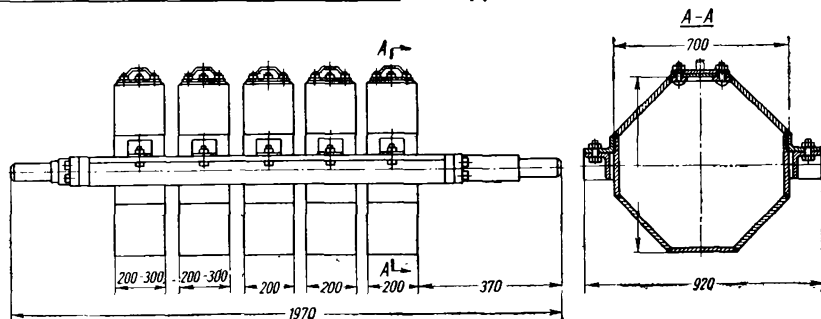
Барабан для мокрой галтовки мелких поковок (секционный)
